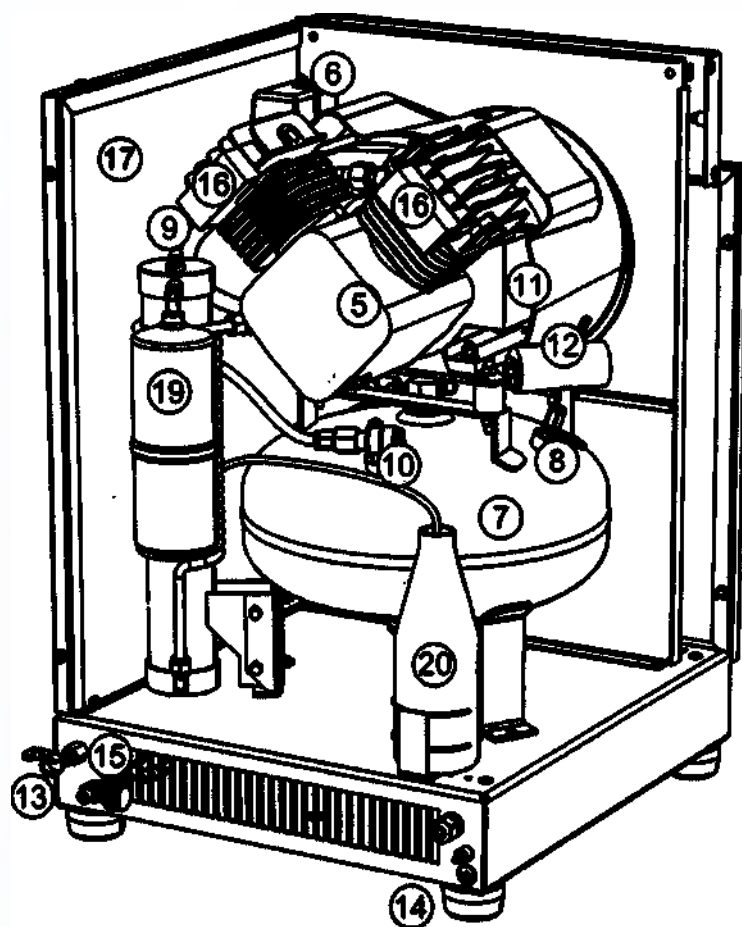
Общий вид компрессора KM-16.VS204KD
